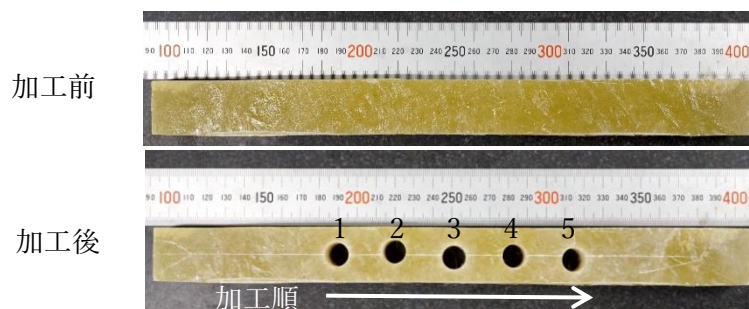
図 GFRP 試験片の加工位置 (上:加工前 下:加工後)
